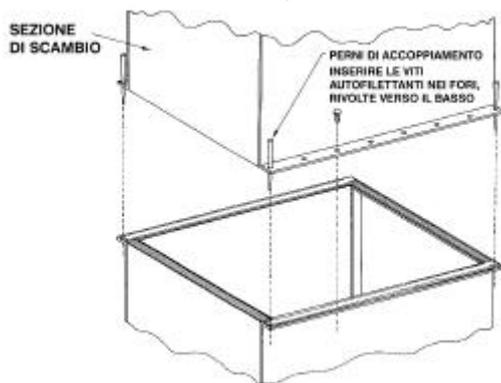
Assemblaggio della sezione ventilante con la sezione bacino
